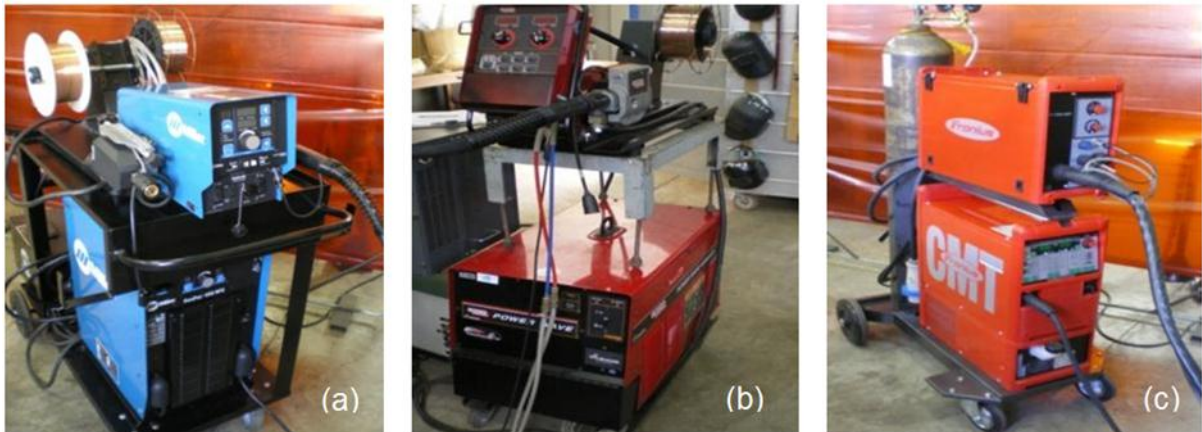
Fontes de soldagem utilizadas, a: Miller; b: Lincoln Eletric; c: Fronius. (Adaptado de Costa (2011))
